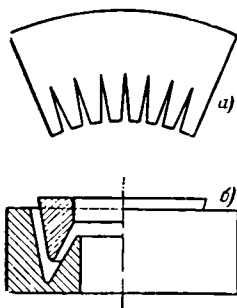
Прессформа и заготовка для миканитового конуса.
